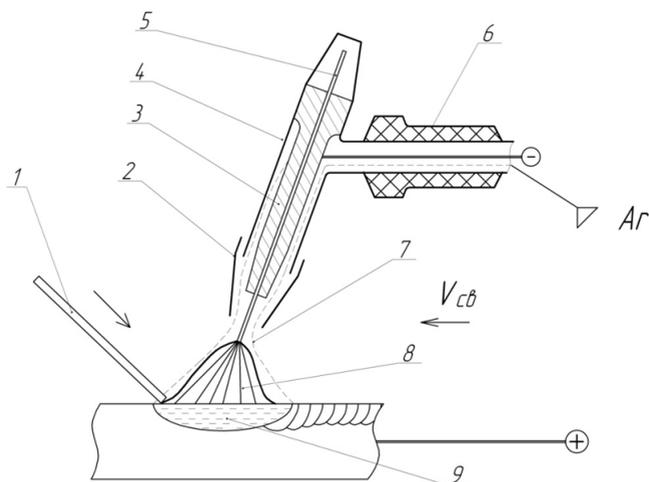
Схема аргонодуговой сварки неплавящимся электродом:
